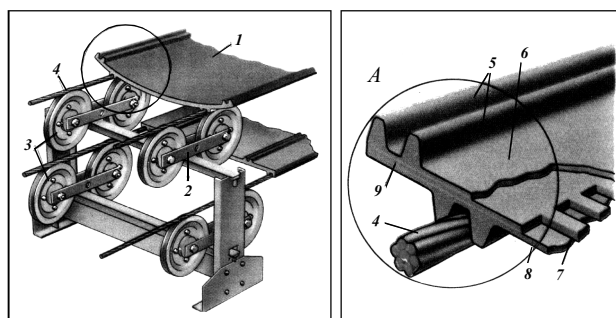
Конструкція лінійної частини стрічково-канатного конвеєра: 1 - стрічка; 2 - балансир роликів; 3 - підтримуючі канат роликів; 4 - тяговий канат; 5 - бічний приплив стрічки; 6 - верхня обкладка стрічки; 7 - поперечна ресора; 8 - нижня обкладка стрічки; 9 - тканинна прокладка.
